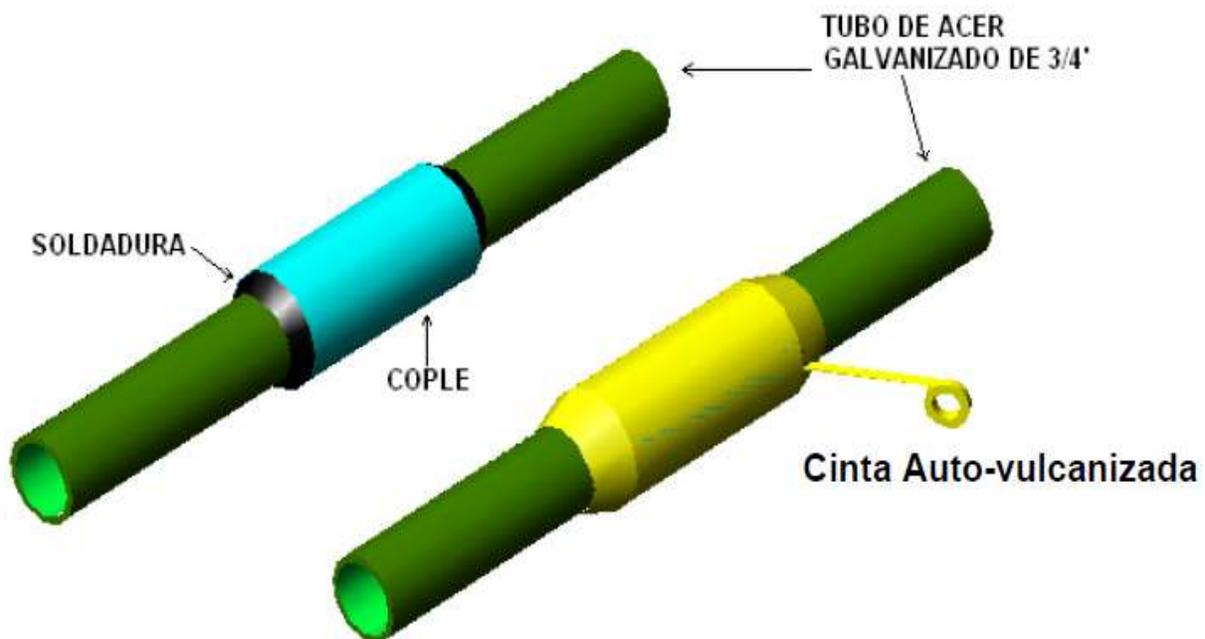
Unión de los tubos de acero galvanizado y aplicación de soldadura.
